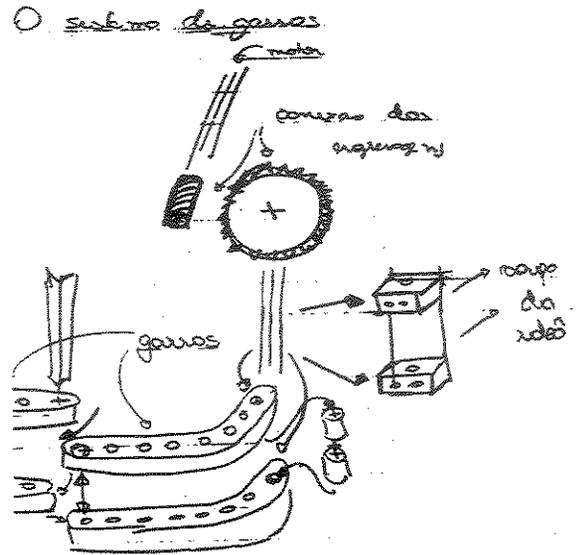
Desenho a mão livre do sistema de garra com engrenagem e rosca sem fim
